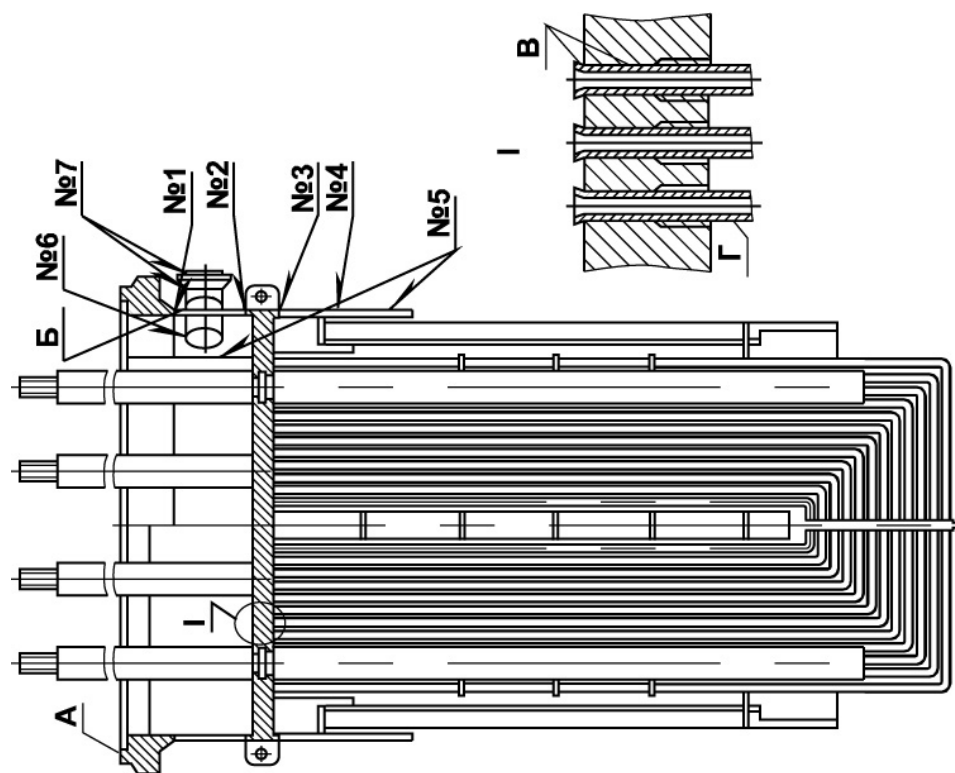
Сварные швы трубного пучка ПНД:
